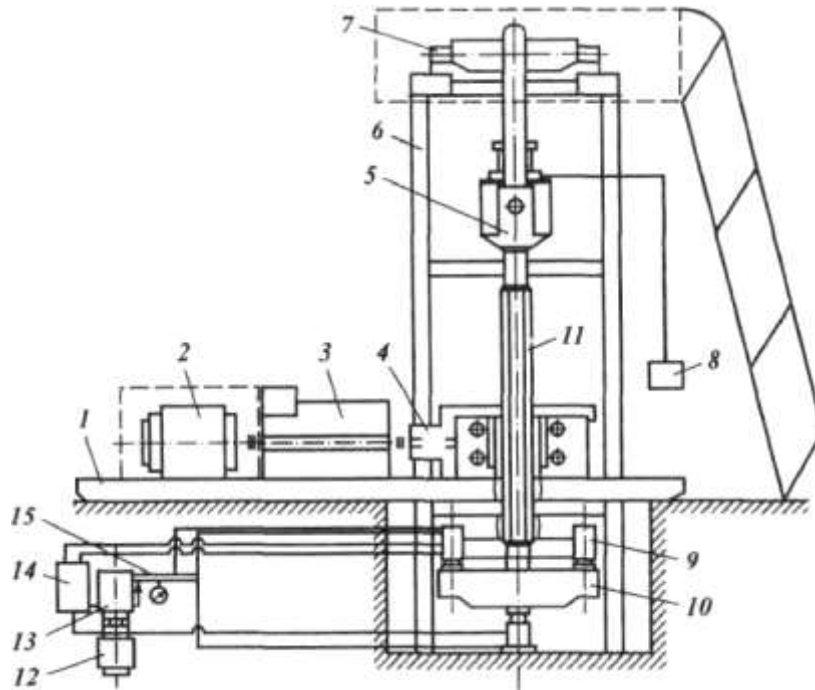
Схема стану для обкатки вертлюгов: 1 - рама;
